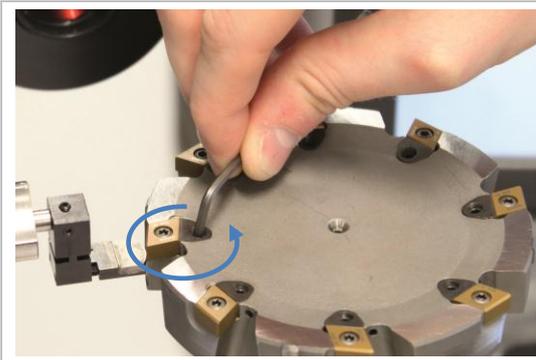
Gewindespindel gegen den Uhrzeigersinn drehen
